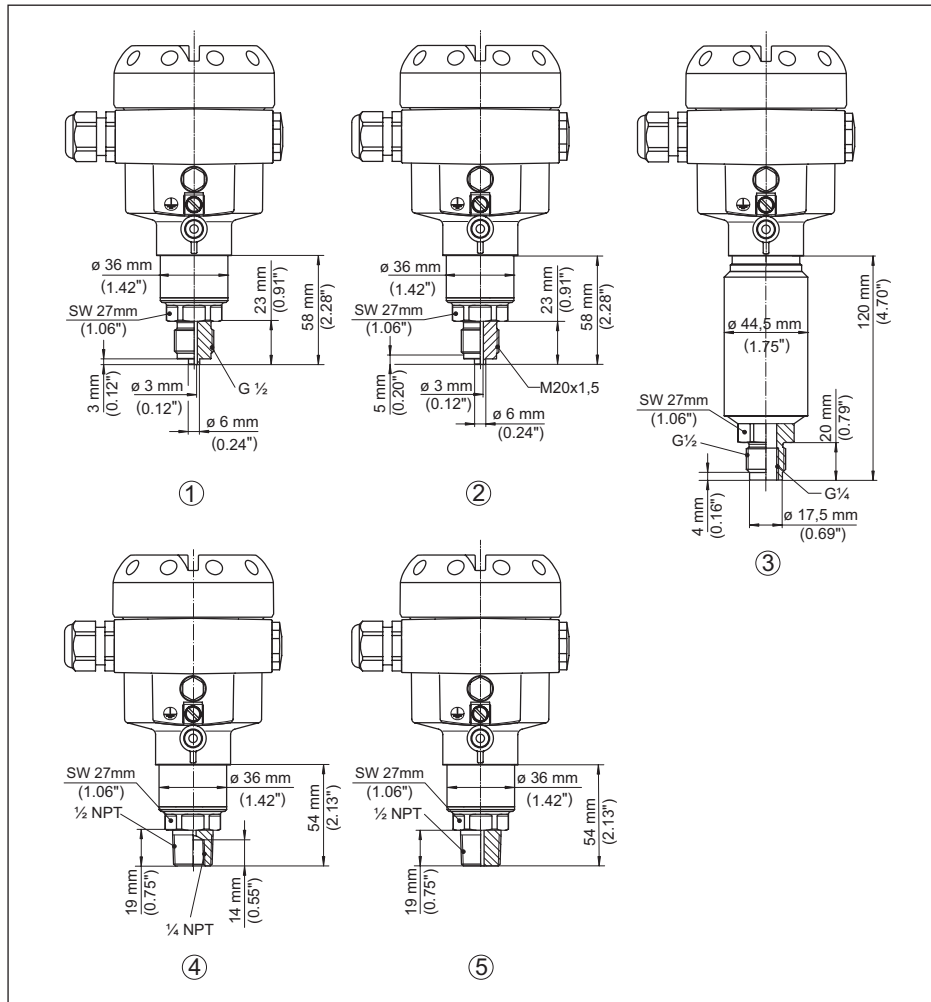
IPT-2x, Gewindeanschluss nicht frontbündig
